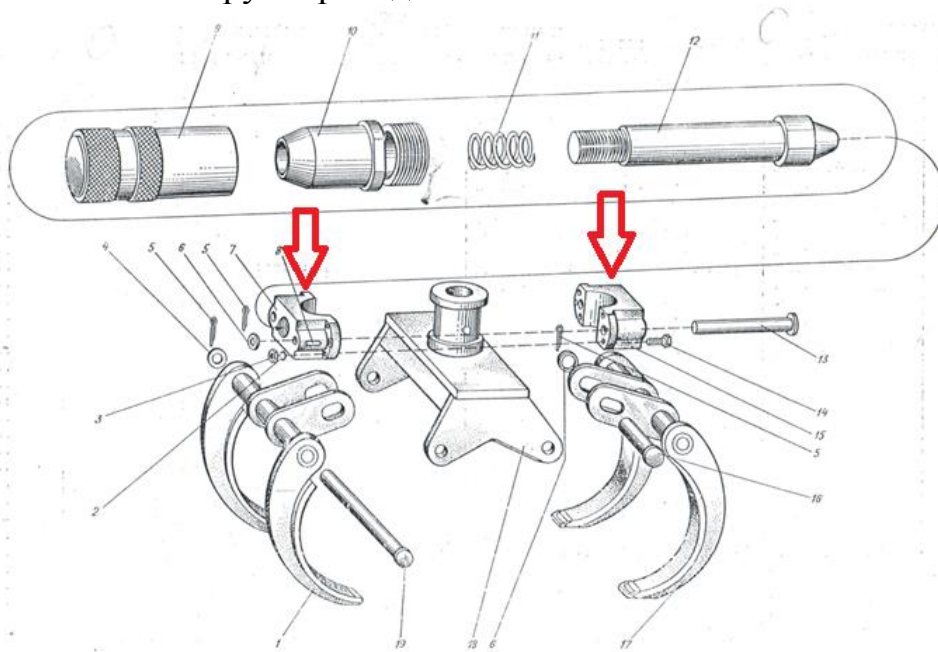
Вилочний захват ПКУ (корпуси виділені червоним)
